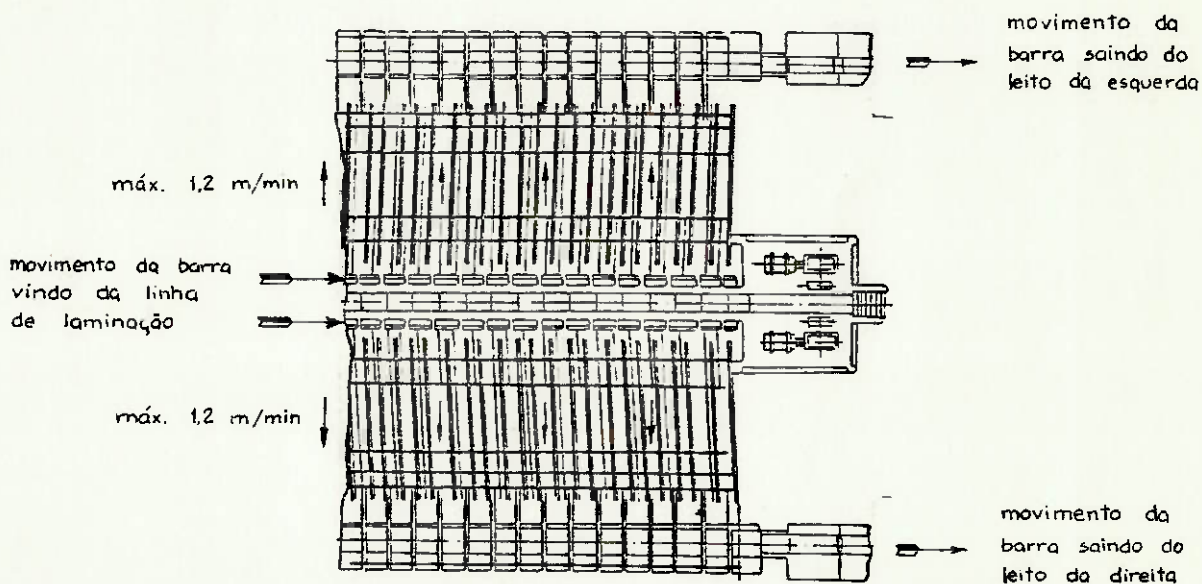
Vista de Planta de um Leito de Dois Lados (Perfis Leves)
